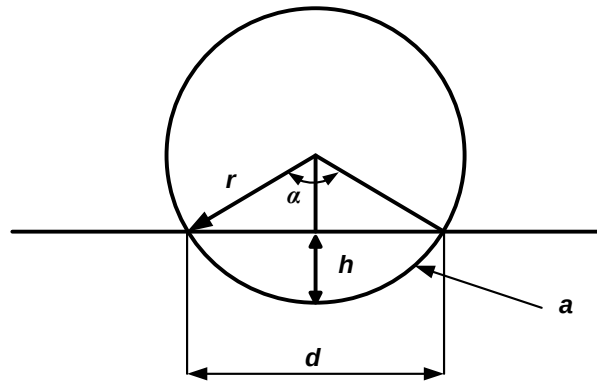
Утворення площі вдавлювання на поверхні циліндричної деталі
